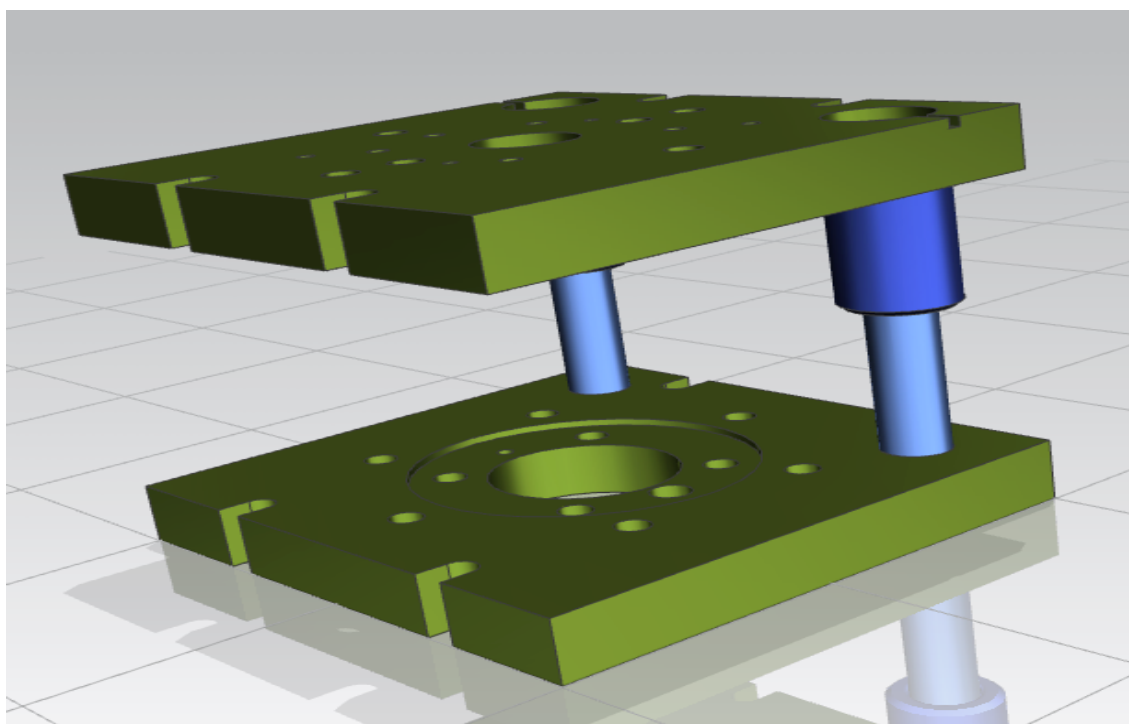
Сборка Блок штампов – Assemblies.prt
